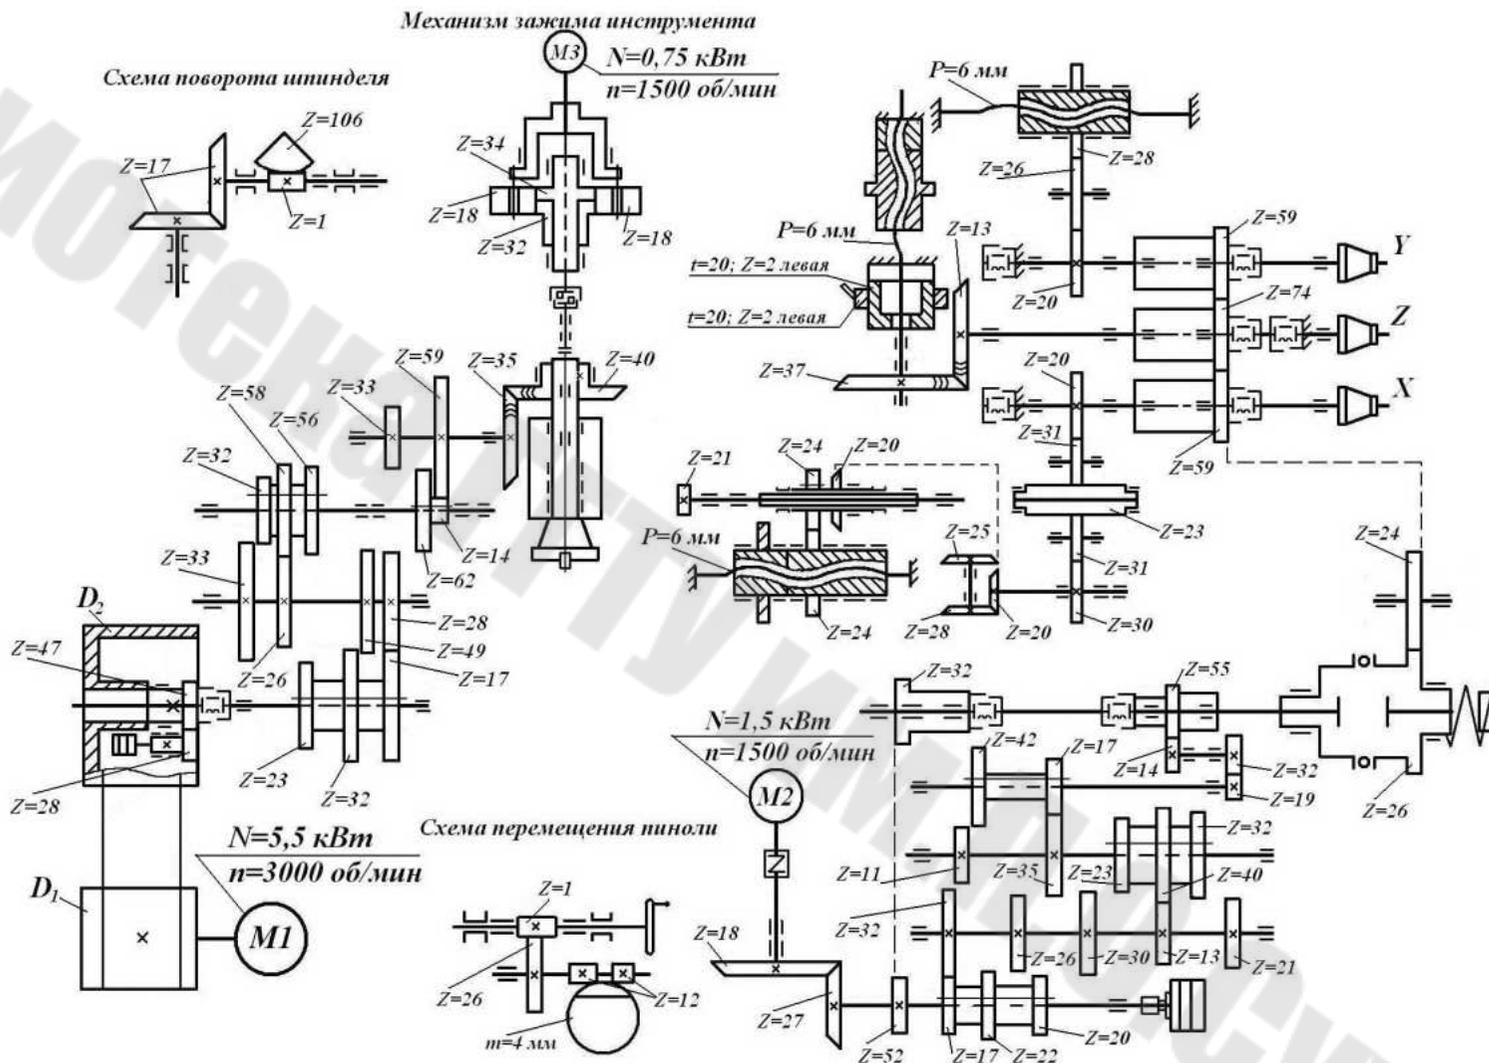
Схема кинематическая принципиальная станка FSS350R
